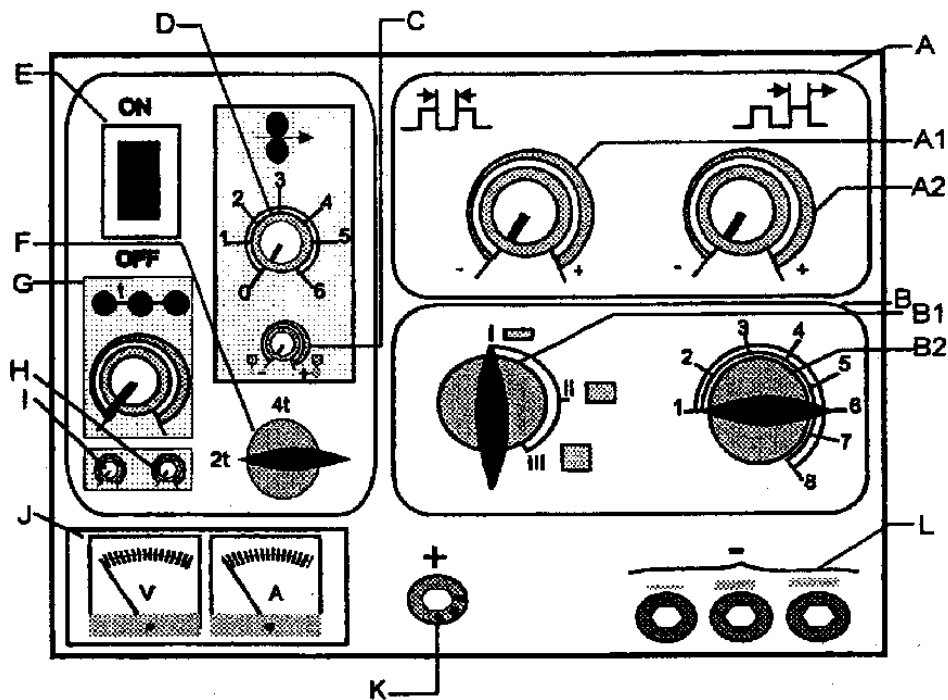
PANEL DE CONTROL DE UNA MÁQUINA COMPACTA
